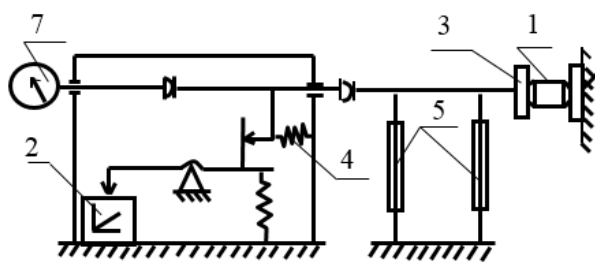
Вимірювальний пристрій для контролю довжини деталі
